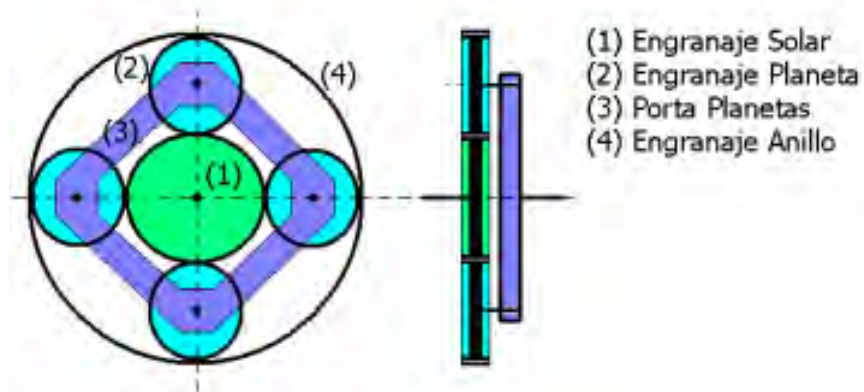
Partes de un tren de engranes planetarios ^[12]
